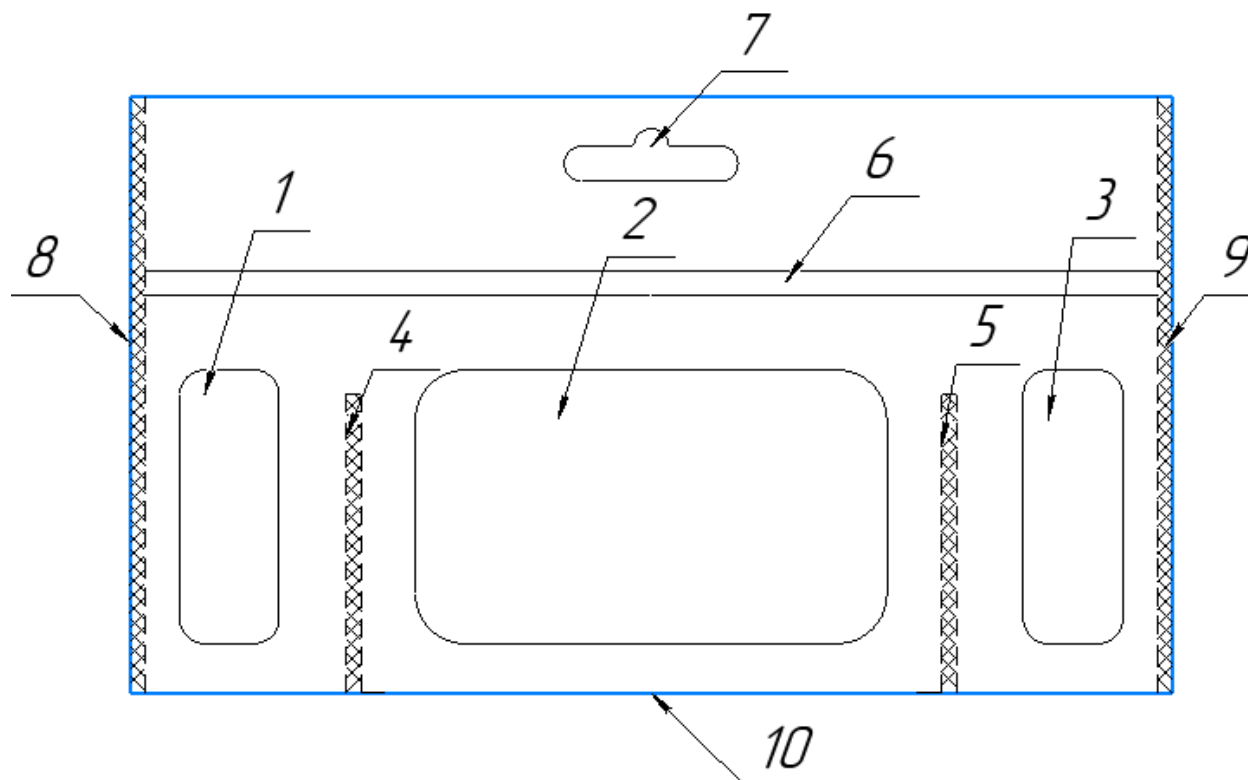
Конструкція готової упаковки (після стадії згину, зварювання швів, вварювання зіп-застібки, та висічки єврослоту): 1, 2, 3 – прозорі віконця; 4, 5 – зварні шви, які розділяють між собою порожнини для гаджетів; 6 – зіп-застібка; 7 – єврослот; 8, 9 – бокові зварні шви, які формують упаковку.
